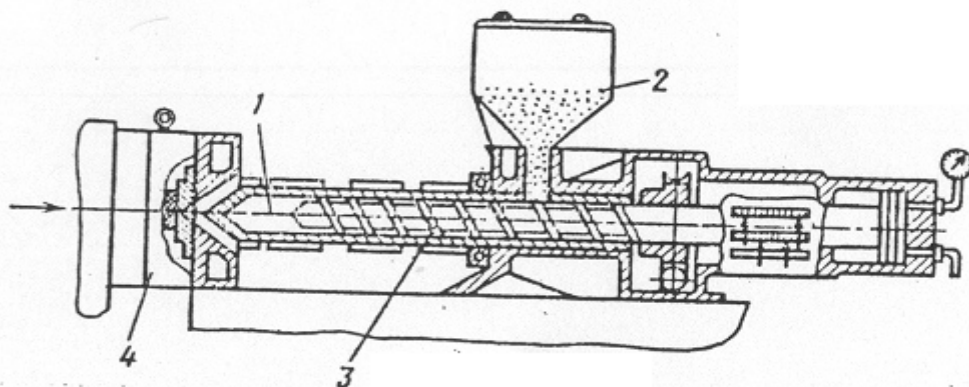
Схема установки для изготовления пенополистироловых моделей под давлением: 1 – рабочий цилиндр; 2 – гранулы полистирола; 3 – прессующий поршень; 4 – пресс-форма.
